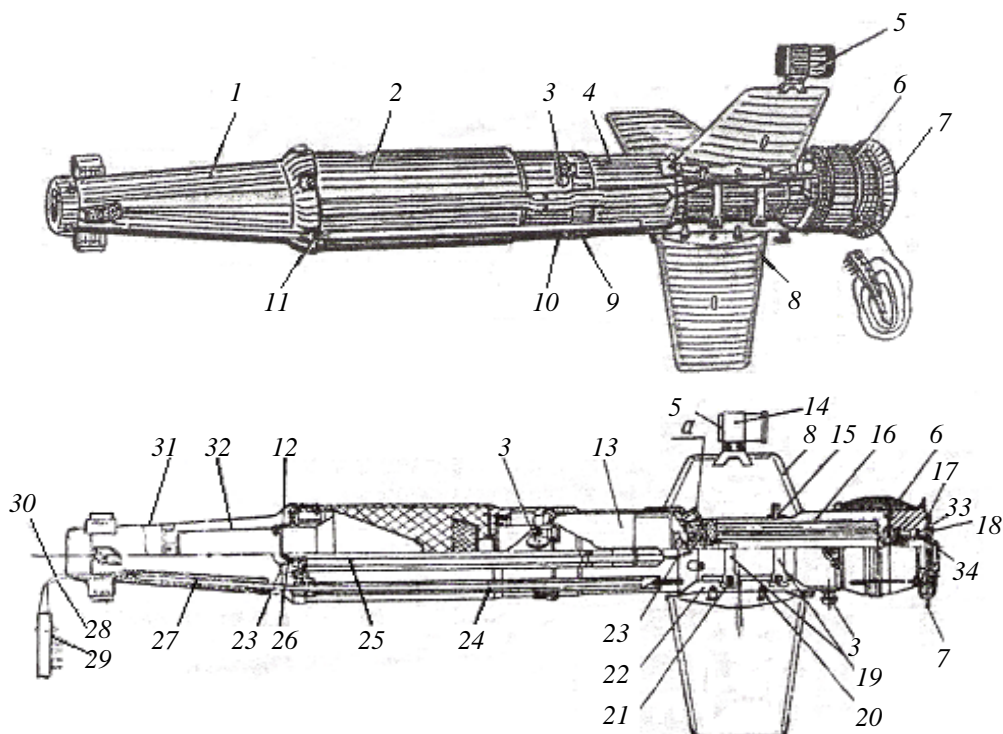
Ракета 9М116: 1 – блок рулевого привода; 2 – боевая часть; 3 – винт; 4 – двигатель; 5 – трассер; 6 – катушка; 7 – опорное кольцо; 8 – стабилизатор; 9 – накладка; 10, 11 – винты; вид в разрезе: 12 – провод; 13 – камера разгонно-маршевая; 14 – хомутик; 15 – штуцер; 16 – камера стартовая; 17 – накладка; 18 – винт; 19 – хомут; 20 – скоба; 21 – винт; 22 – опора; 23 – обтекатель; 26 – провод; 27 – лирка; 28 – трос; 29 – вилка; 30 – жгут; 31 – конус; 32 – конус верхний; 33 – плата; 34 – гайка; а – сопло
